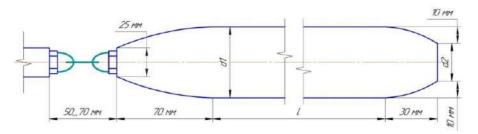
Схема уширителя для кротователя №1 конусоцилиндрической формы Figure 7 — Scheme of the expander for the mole maker No. 1 of a cone-cylindrical shape
